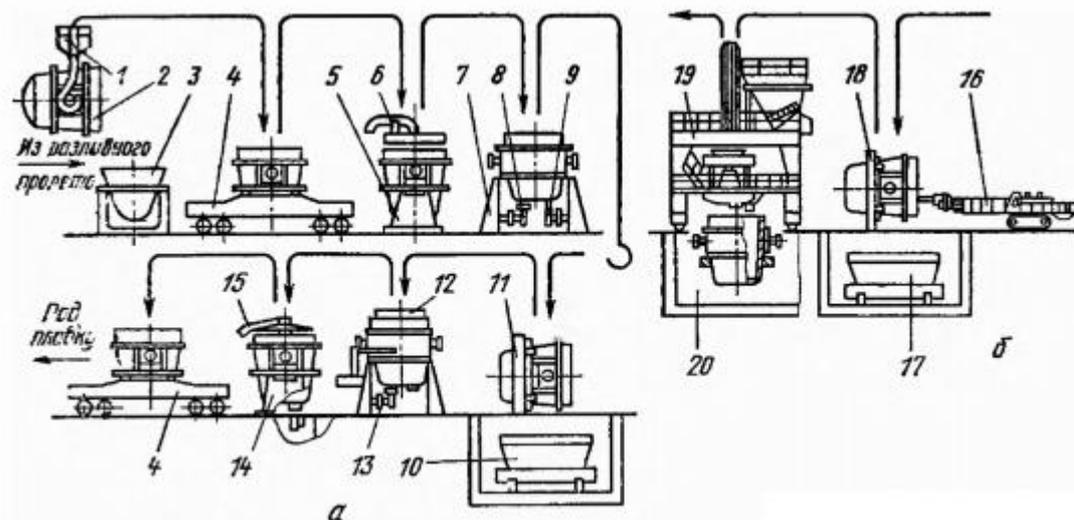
Схема межплавочной подготовки (а) и ремонта (б) сталеразливочных ковшей
